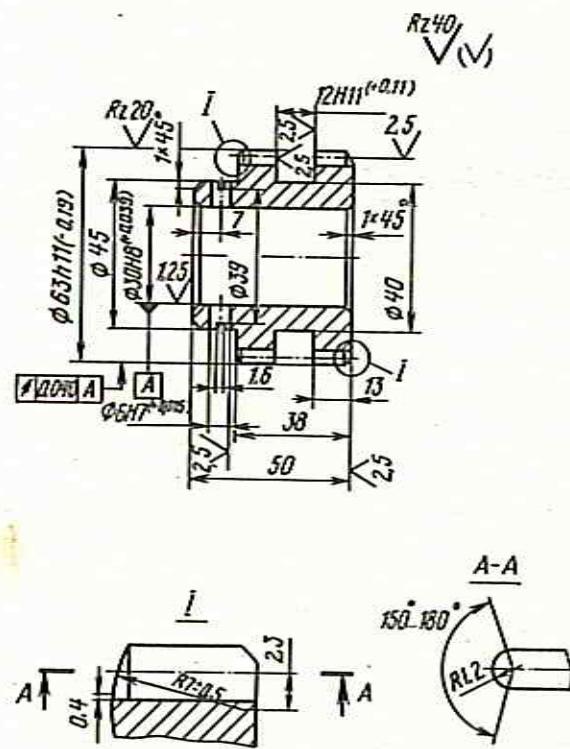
Колесо зубчатое, деталь № 3Л722А.322.402
